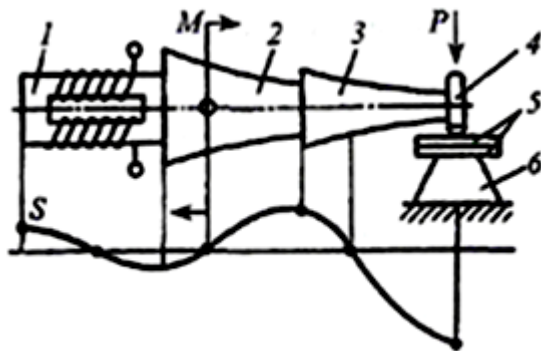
Схема ультразвуковой сварки: 1-
